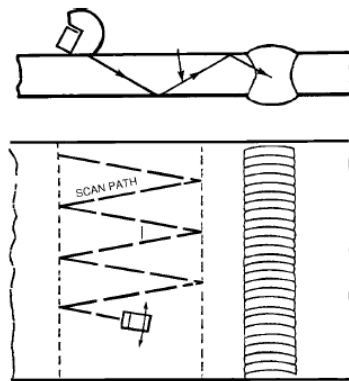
Técnica de inspección de soldaduras a tope con haz angular (ASTM International, 1994).
